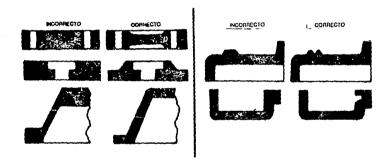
Alternativas de diseño para mantener un espesor uniforme de la accción del producto. (Ref. 5).
